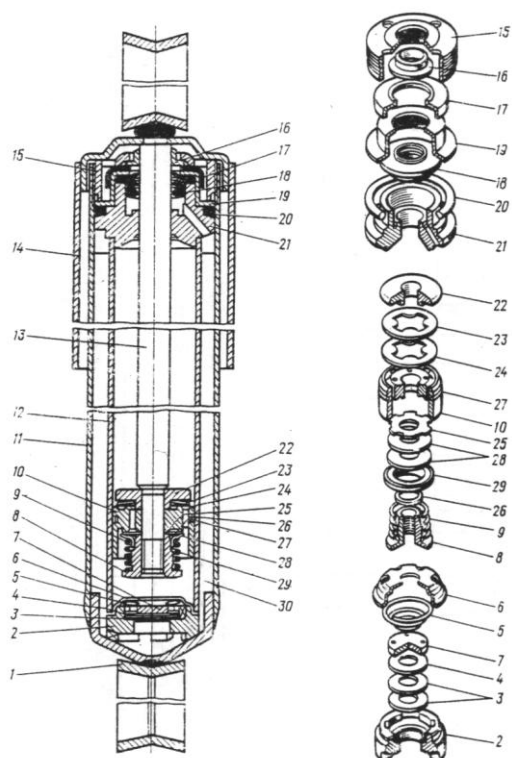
Амортизатор задней подвески автомобиля ВАЗ-2121
